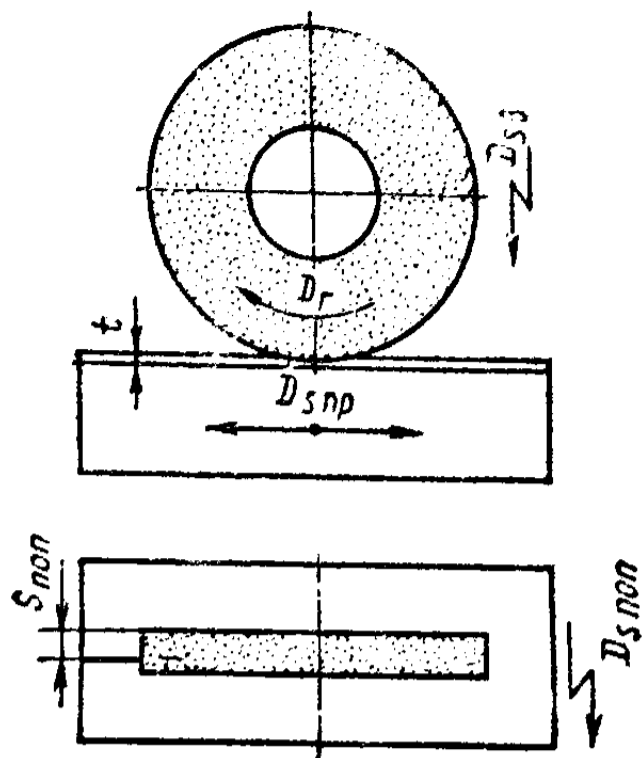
Схема обработки заготовки на плоскошлифовальном станке периферией круга
